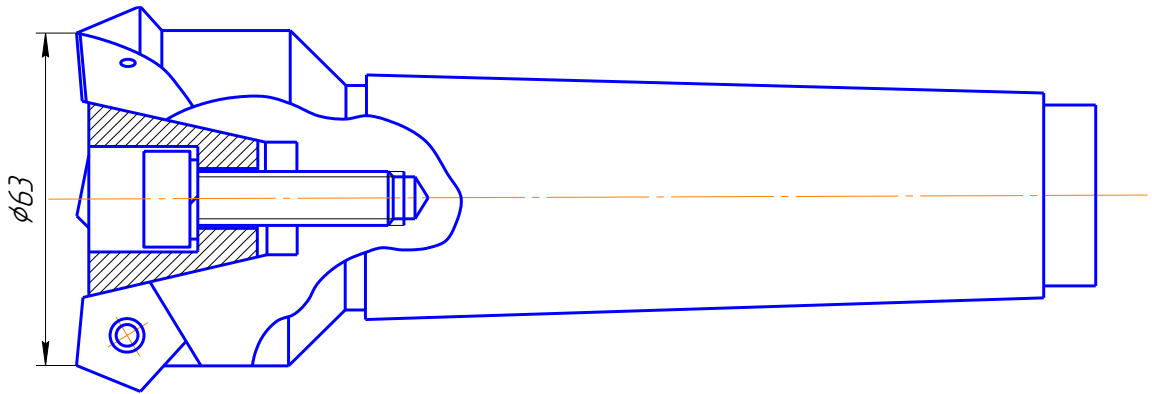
Фреза торцева хвостова ТУ 2-035-476-76
